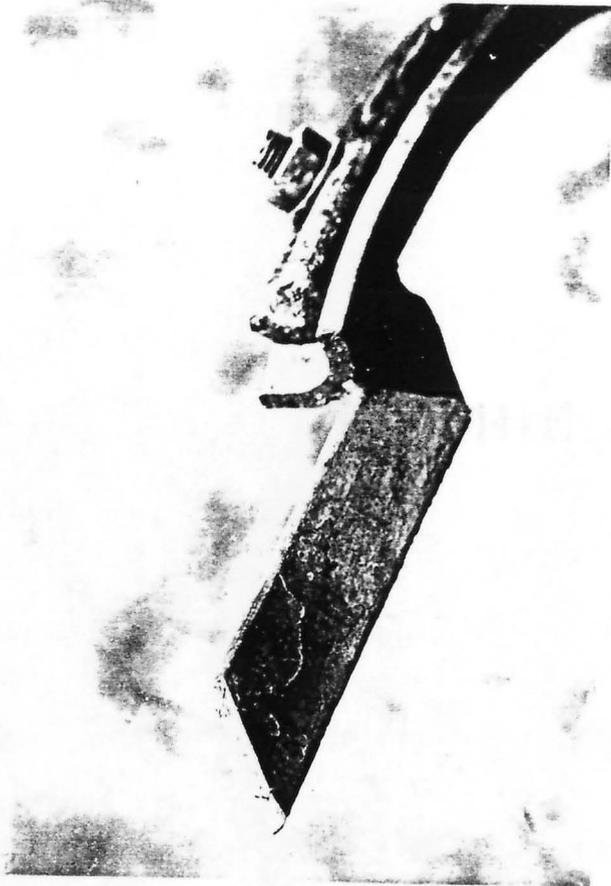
Puntilla soldada a la herramienta tipo cincel
